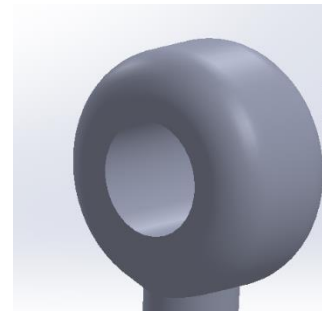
Vista detalle de mosquetón pieza N°70 parte superior (Fuente 108)
